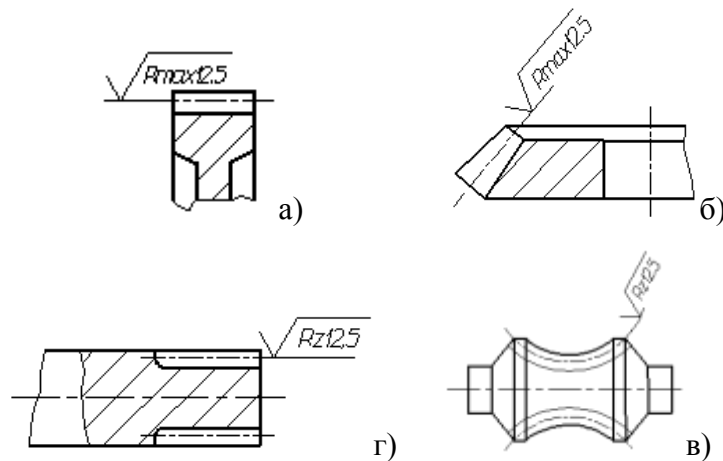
Обозначение шероховатости рабочих поверхностей зубьев зубчатых колес (а, б, в) и шлицев (г)
